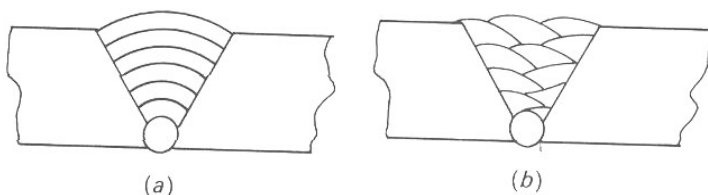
As técnicas de soldagem de (a) trançar e (b) filetar
